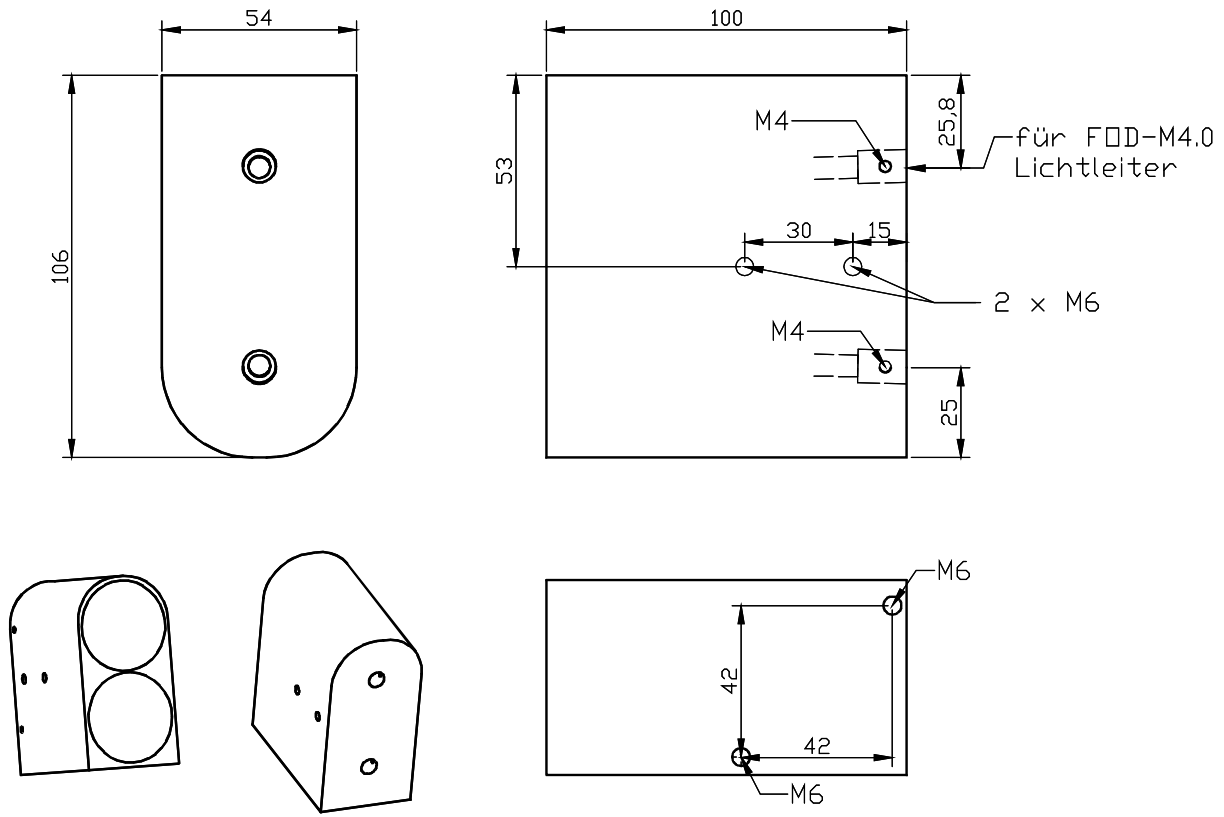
Technische Zeichnung FOD-M4.0-1100 | Technical Drawing FOD-M4.0-1100
